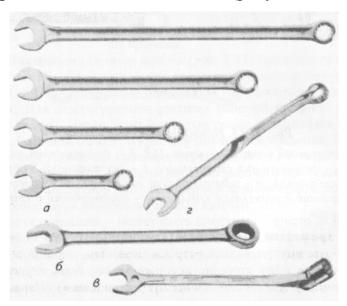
Комбинированные гаечные ключи: a — различной длины (сверхдлинные, удлиненные, стандартные, укороченные); δ — с храповым механизмом в накидной головке; ϵ — с шарнирной торцевой головкой; ϵ — твистер
